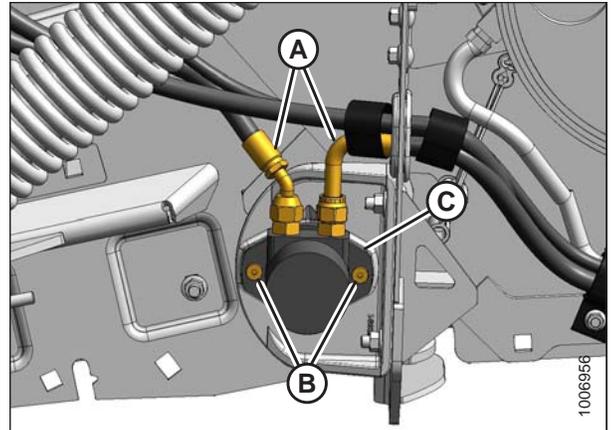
Motor hidráulico trasero; lado izquierdo
